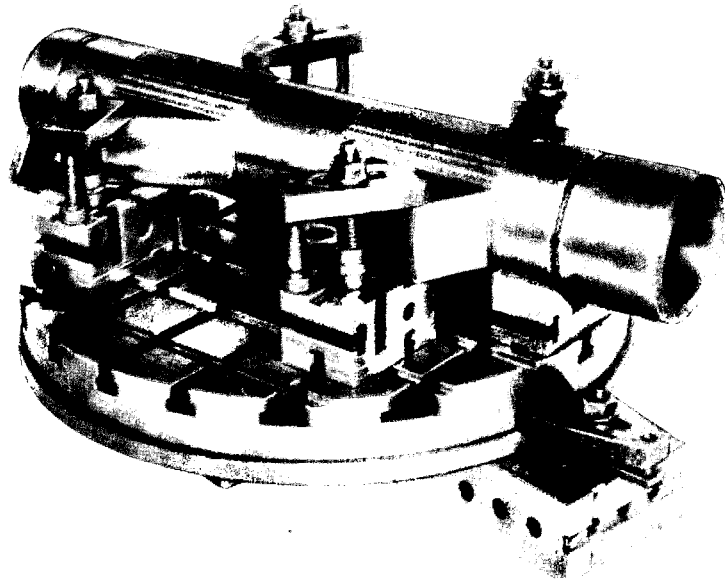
Приспособление поворотное для растачивания каналов стойки на горизонтально-расточном станке
